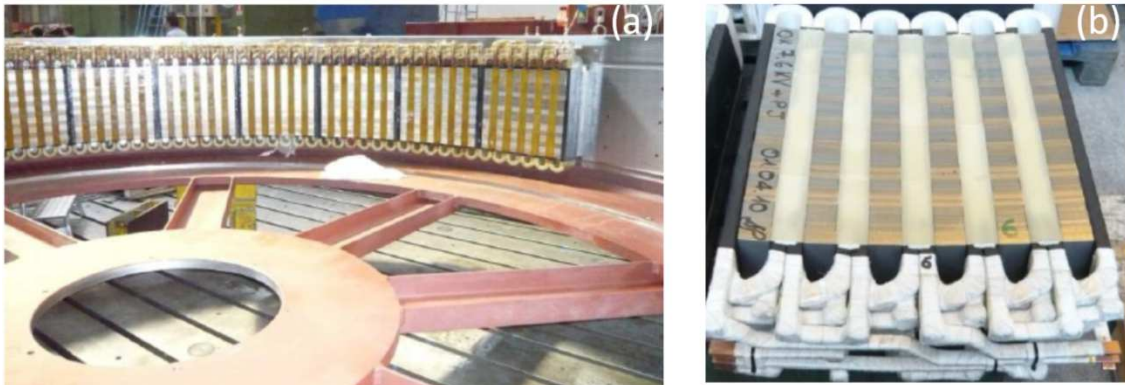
a) statore durante il montaggio b) singolo modulo di statore.
